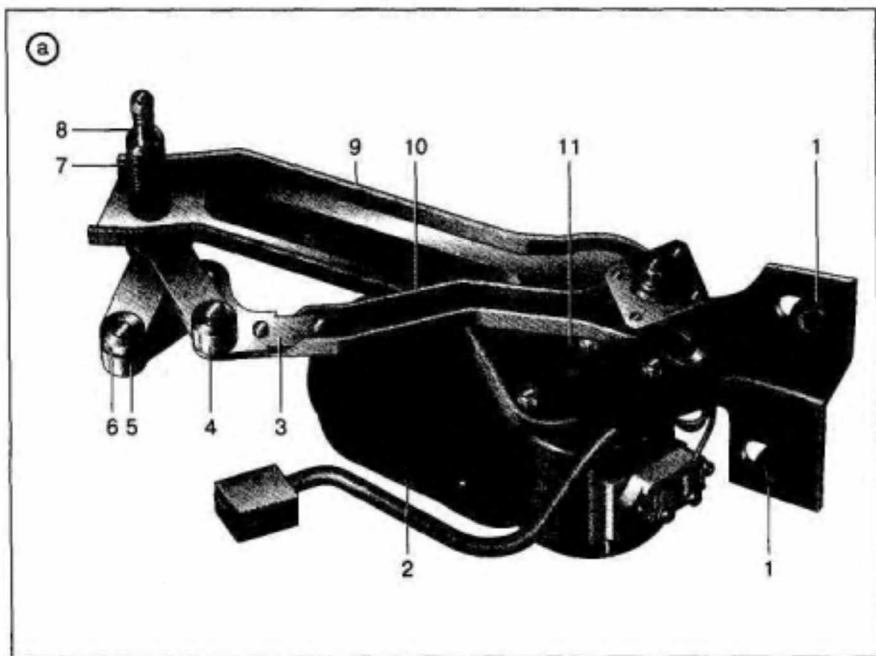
а. Общеустройство стеклоочистителя: 1 — резиновая втулка; 2 — электродвигатель; 3 — наконечник промежуточного рычага; 4 — качающийся рычаг; 5 — шатун; 6 — рычаг; 7 — штуцер оси рычага; 8 — ось рычага; 9 — кронштейн привода; 10 — промежуточный рычаг; 11 — кривошип
